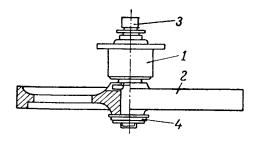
Подающий узел. 1 — корпус подшипника; 2 — маховик; 3 — вал; 4 — гайка.
